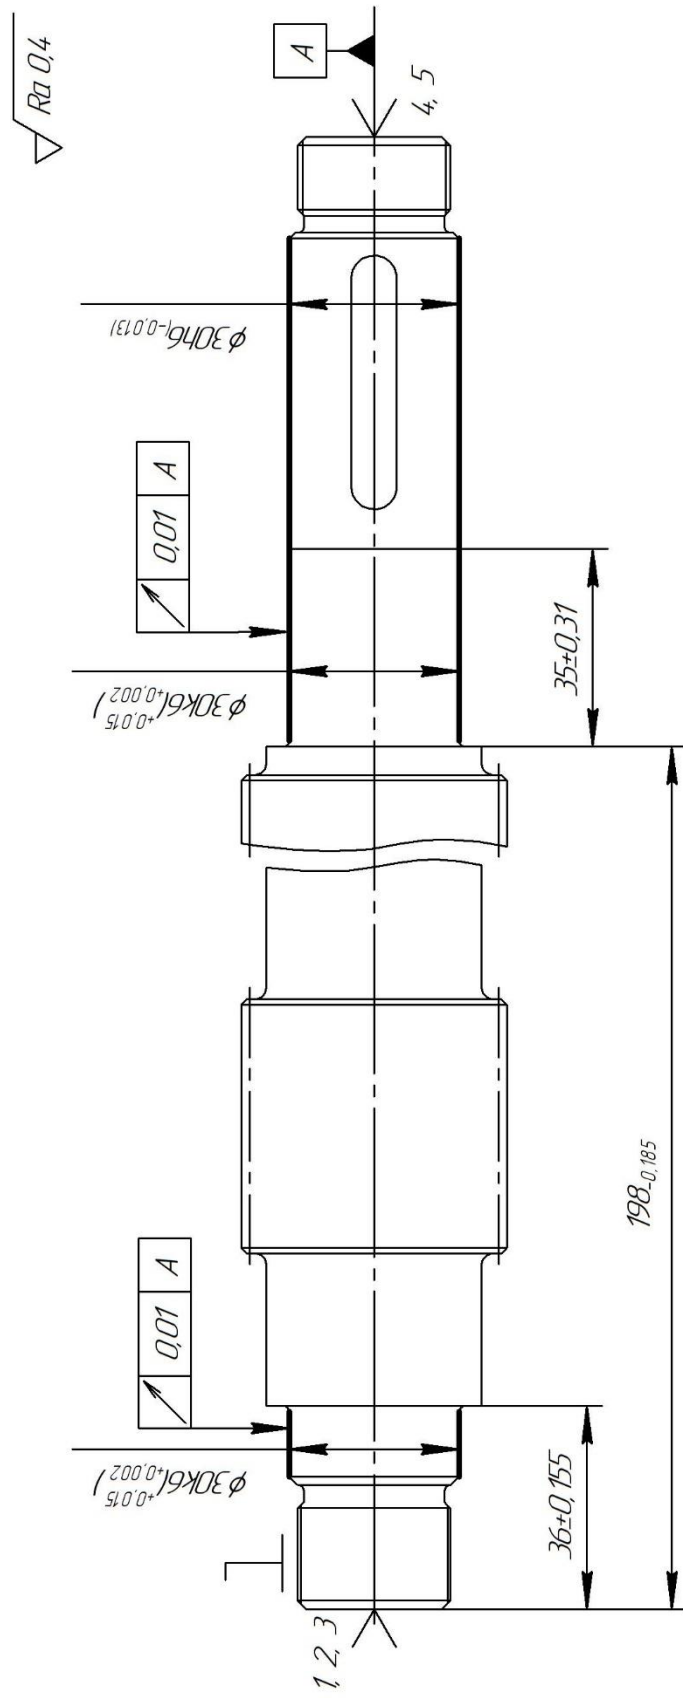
Схема базування заготовки на операції 075 круглошліфувальній
